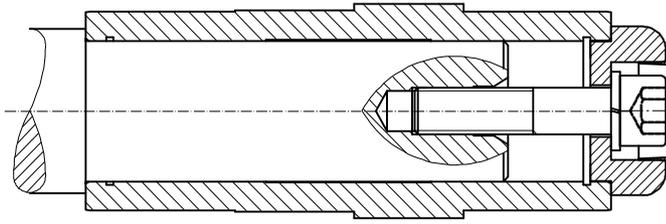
Крепление редуктора к валу с упором с помощью крепежного элемента
